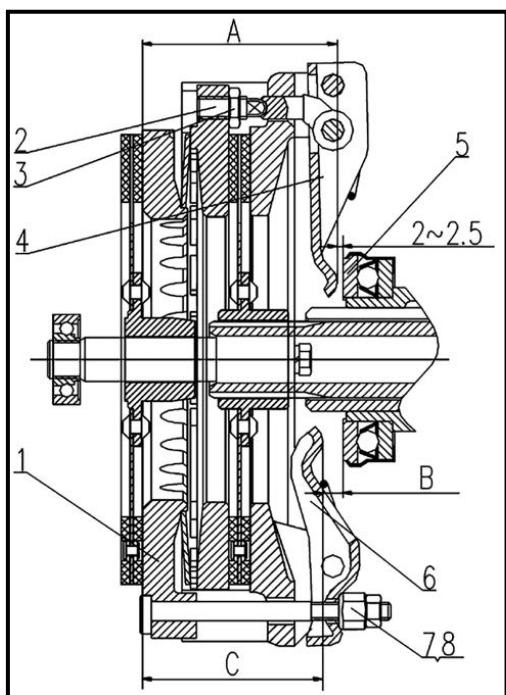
Двухдисковое двухступенчатое сцепление:
